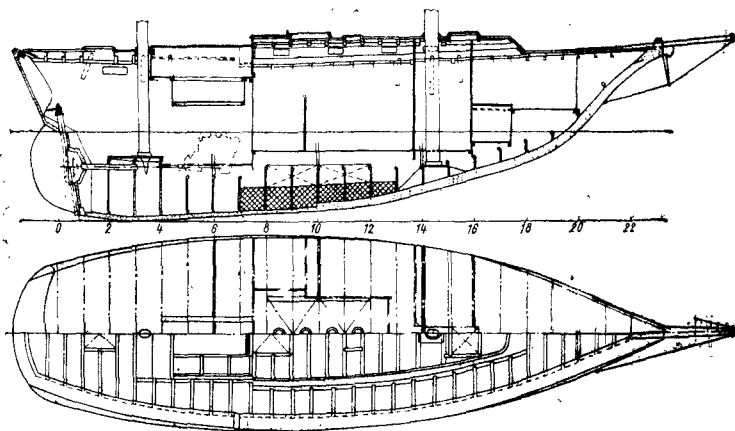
Коиструктивный чертеж кэча из армоцемента.
